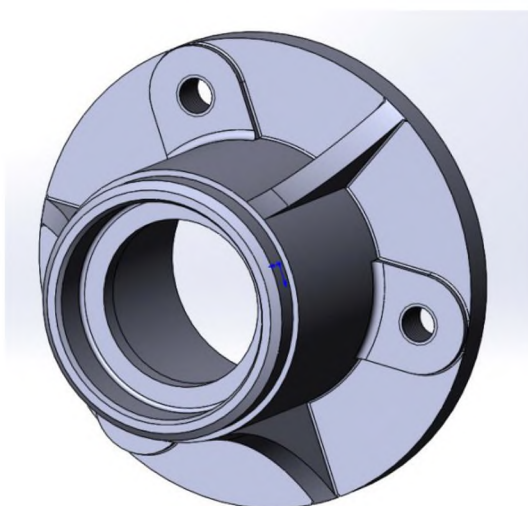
Тривимірна модель корпус Н 109.02.101
